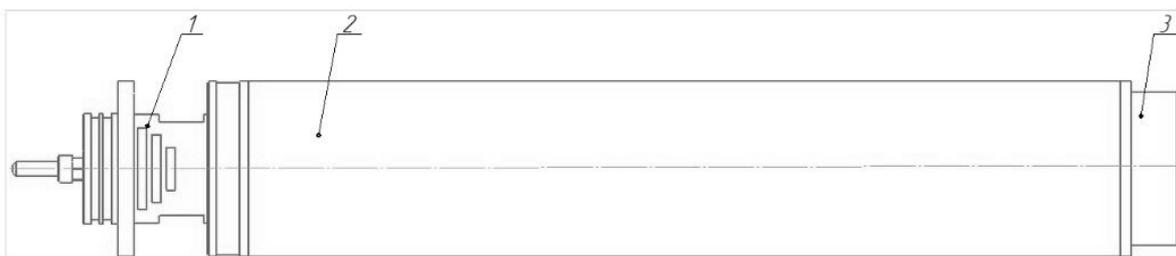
Корпус БП: 1-головка; 2-гильза; 3-заглушка
